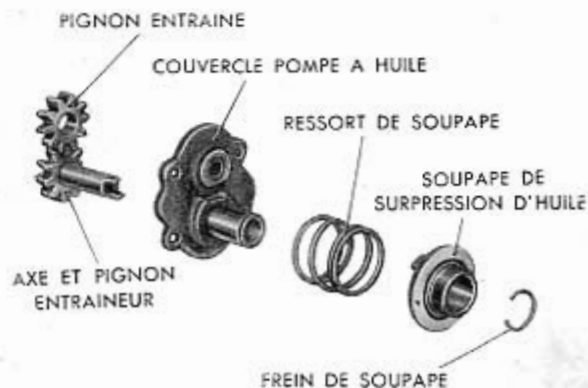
Vue éclatée de la pompe à huile et de la soupape de surpression.
